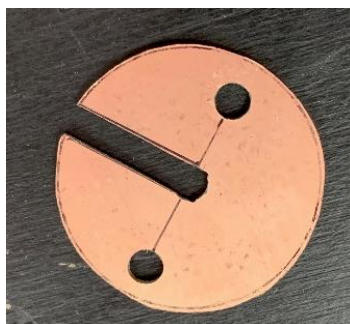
Pieza aislante con ranura. (Plano PL_01_03).[Autor]
